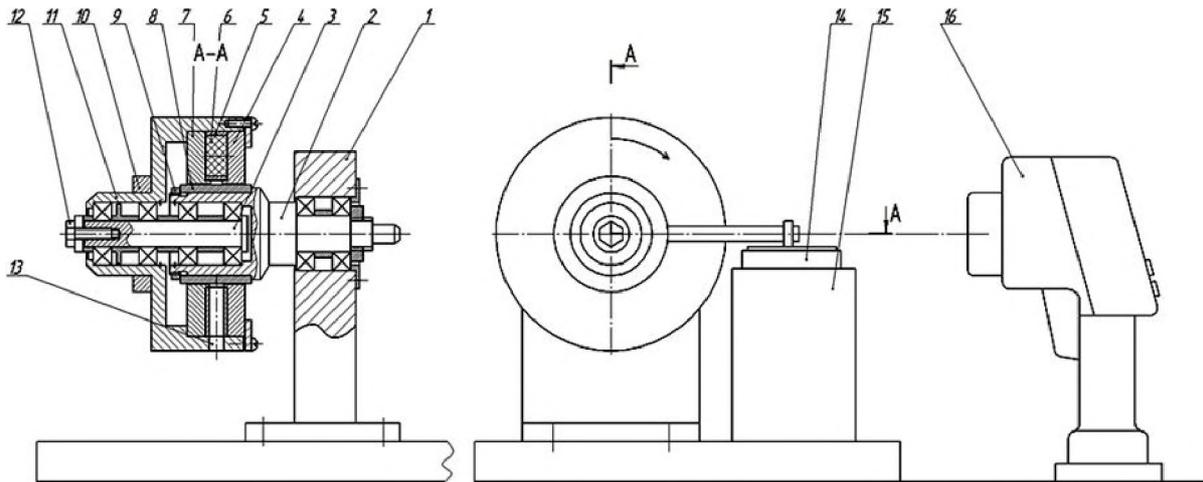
Схема экспериментальной установки: 1 – стойка; 2 – подвижный вал; 3 – неподвижный вал; 4 – съемный полюс; 5 – диск (обойма); 6 – магнит; 7 – съемный полюс; 8 – сменная втулка; 9 – гайка; 10 – хомут; 11 – корпус; 12 – болт; 13 – отверстие для измерения температуры; 14 – весы; 15 – стойка; 16 – тепловизор
